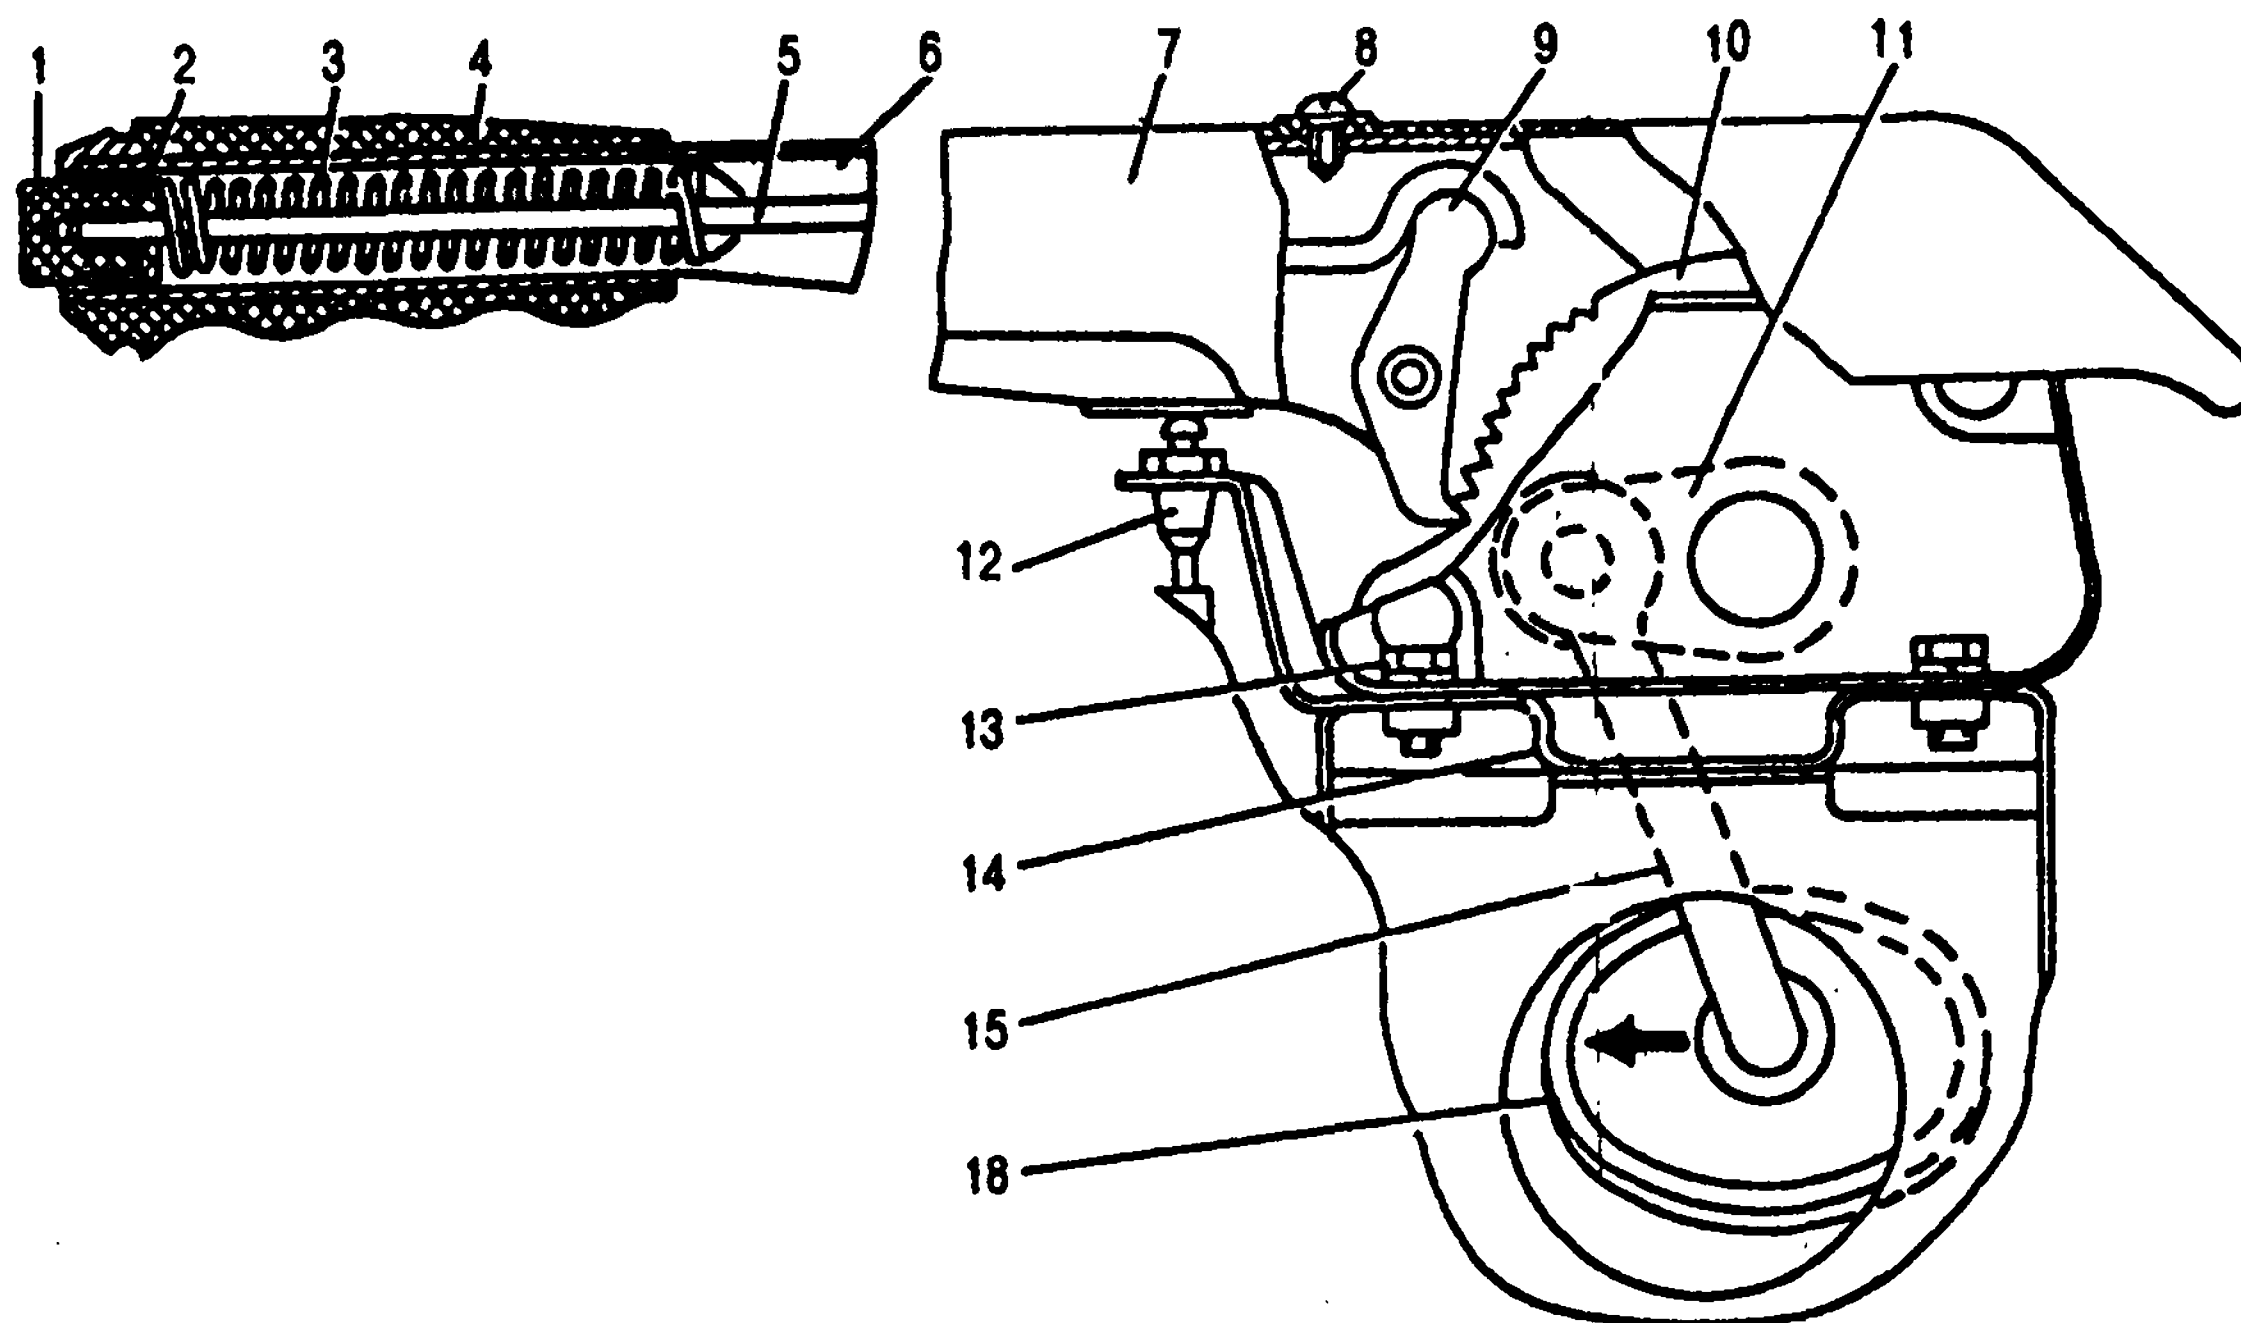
Механизм стояночного тормоза: 1 - кнопка; 2 - шайба; 3 - пружина; 4 - ручка; 5 - тяга собачки; 6 - рычаг; 7 - декоративная облицовка; 8 - винт; 9 - собачка; 10 - зубчатый сектор; 11 - возвратный рычаг; 12 - выключатель; 13 - болт; 14 - переходный кронштейн; 15 - тяга рычага; 16 - уплотнитель тяги
